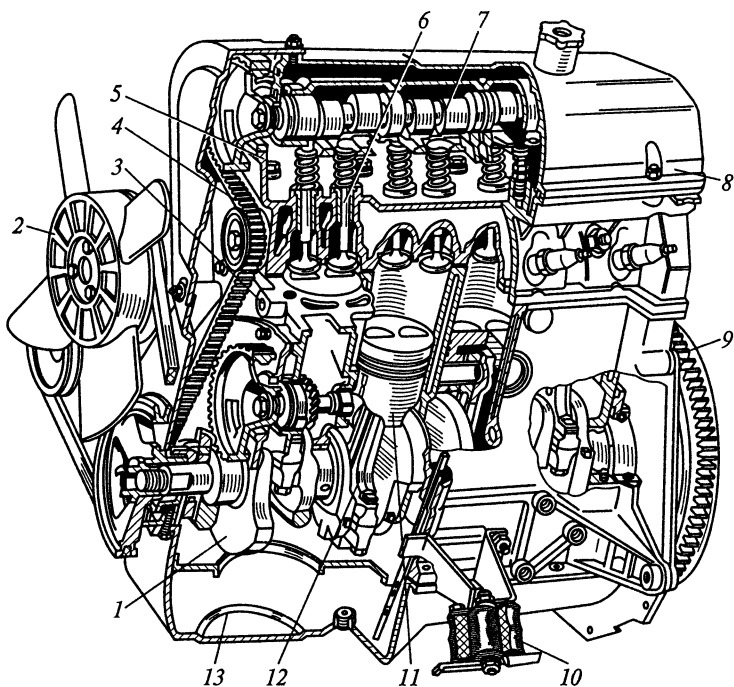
Двигатель легкового автомобиля малого класса:
